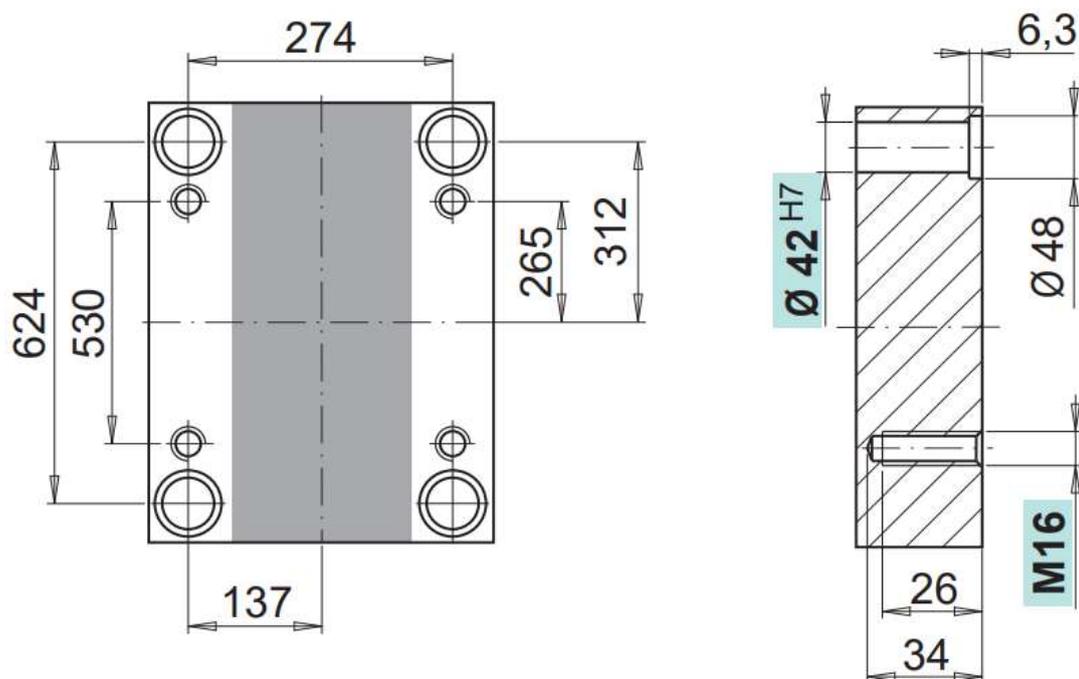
Dimensiones generales de las placas de cavidad de portamoldes MEUSBURGER de 346x696. Extraído de (6).
